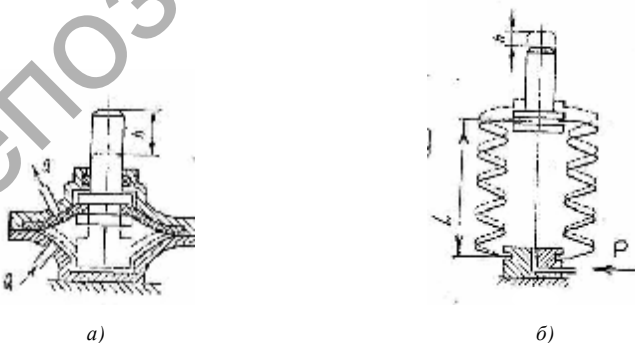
Гидродвигатели поступательного движения: мембранный (а); сильфонный (б)
